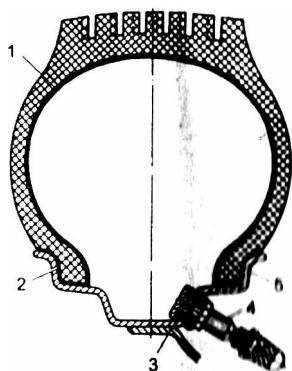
Бескамерная шина: 1 — воздухопроницаемый резиновый слой; 2 — уплотнительный резиновый слой; 3 — ушко жгута; 4 — вентиль; 5 — обод
